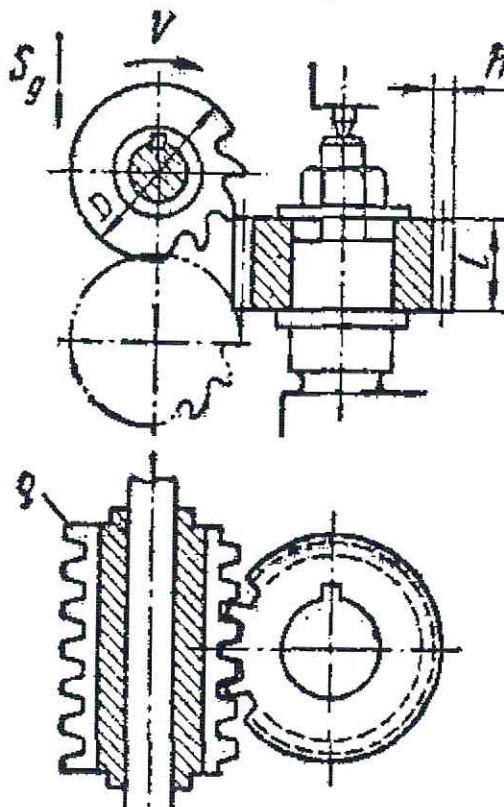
Схема обработки зубьев червячной модульной фрезой.
